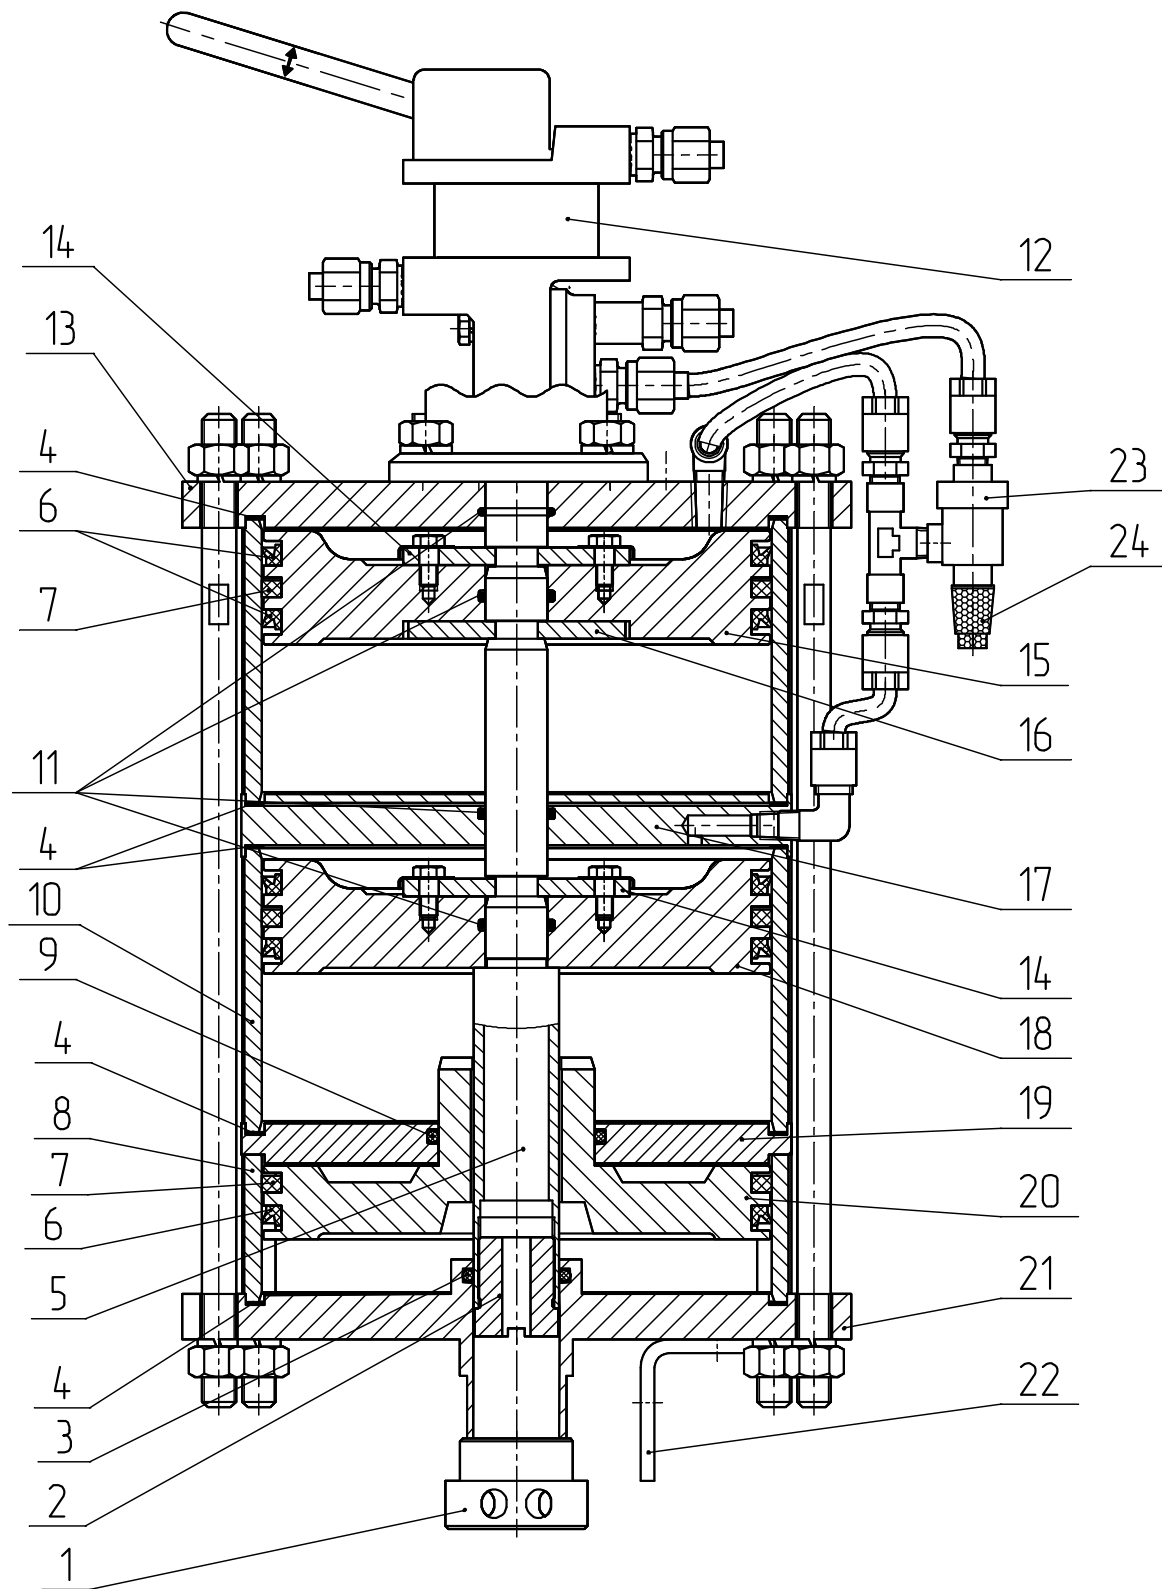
Конструкция трехпоршневого пневмоцилиндра (с клапанами быстрого выхлопа)
